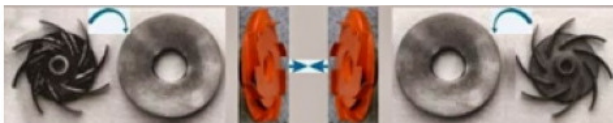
Сборка составных частей сварного рабочего колеса с лопастями, имеющими укороченный профиль
